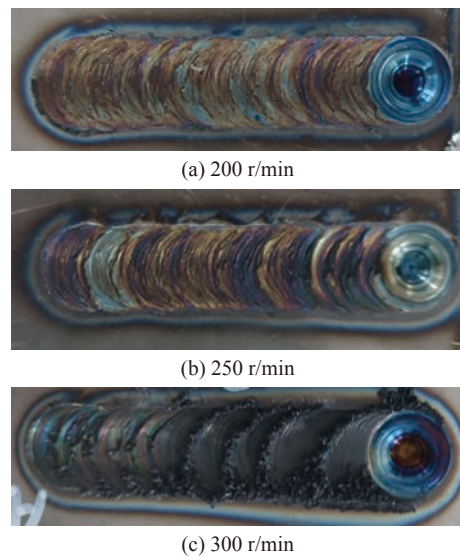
不同焊接工艺参数下的 FSW 焊缝表面形貌
